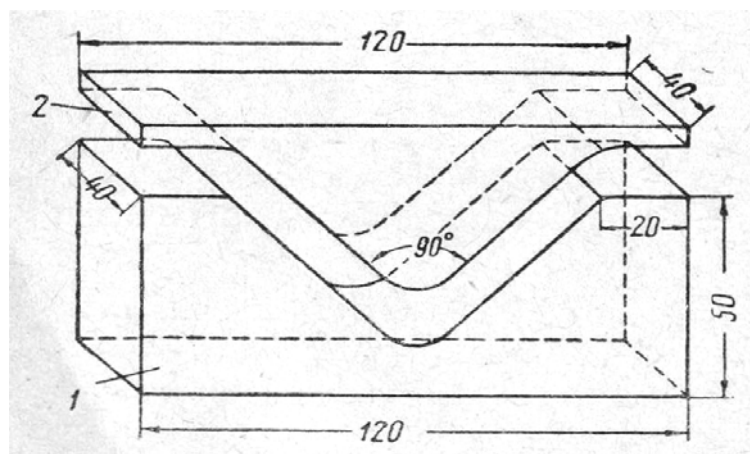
Схема прибора для формования образцов пласткожи для задников
